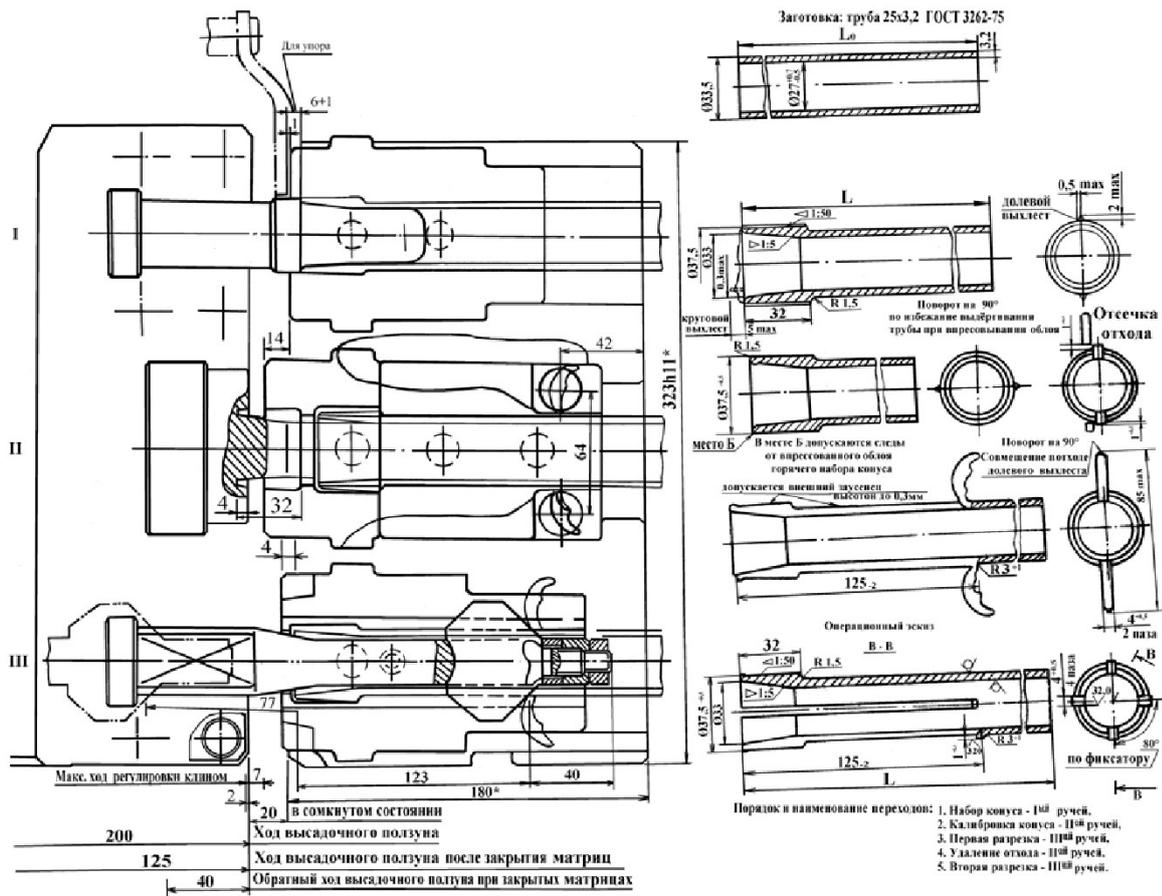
Настройка ГKM для штамповки цанги: 1 - набор конуса в 1-ом ручье; 2 - калибровка конуса во 2-ом ручье; 3 - первая разрезка в 3-ем ручье; 4 - удаление отхода во 2-ом ручье; 5 - вторая разрезка в 3-ем ручье.
